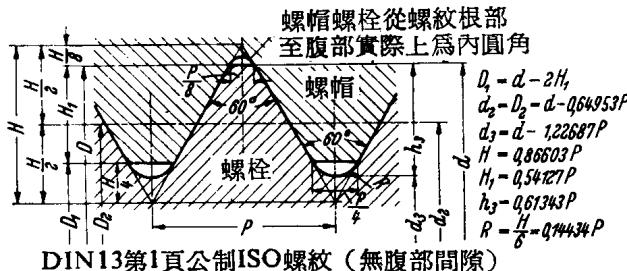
公制ISO螺紋一般螺紋1至68mm直徑之理論數值 DIN 13 第1頁。
